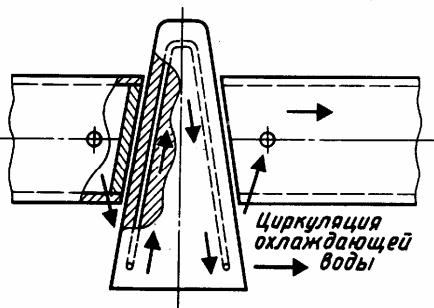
Схема клинового соединения стыка внутреннего формирующего кольца
